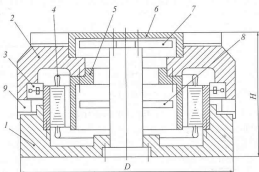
Поворотный стол на базе высокомоментного двигателя:
